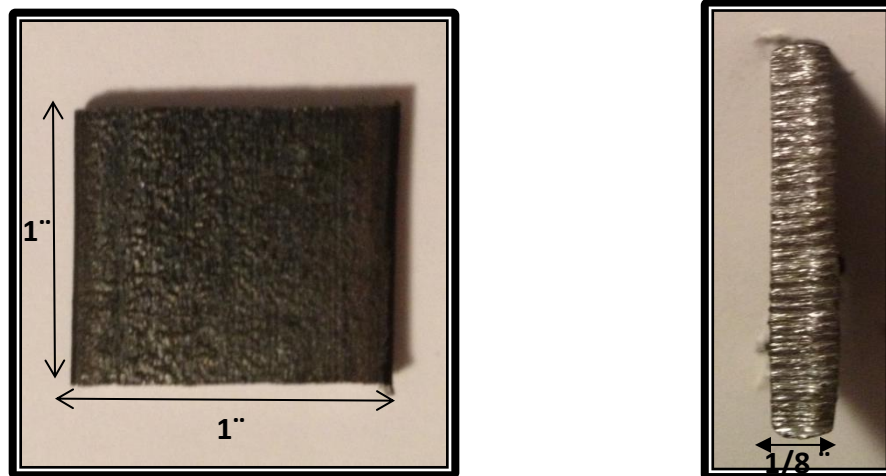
Geometría de las probetas utilizadas en la experimentación.
